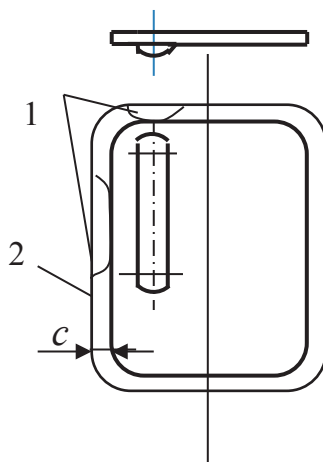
Искривление контура заготовки в связи с утяжкой материала при формовке ребра жесткости:
